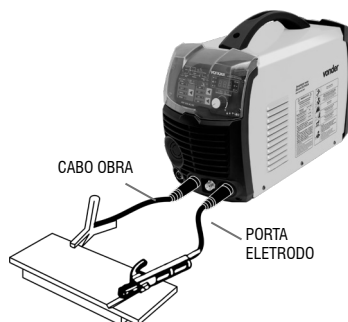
Montagem dos cabos de solda para soldagem de Eletrodo Revestido (MMA)
